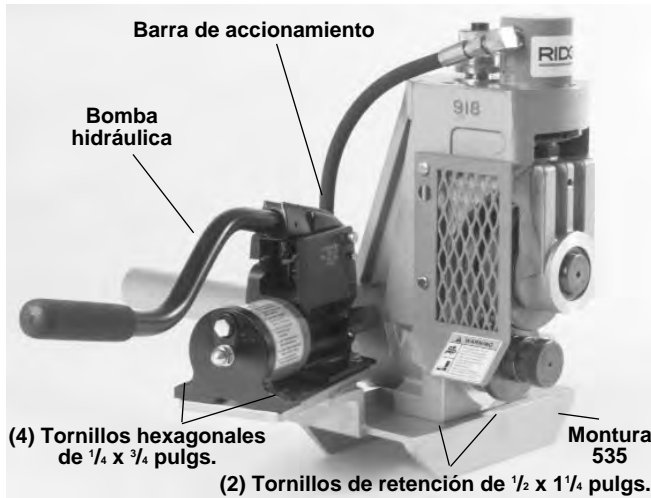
Ranuradora a Rodillos No. 918 puesta sobre la montura de la Máquina Roscadora No. 535
